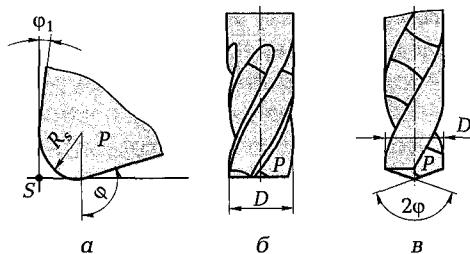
Положение настроечной точки P для различных инструментов: a — для резца; b — для фрезы; $в$ — для сверла
